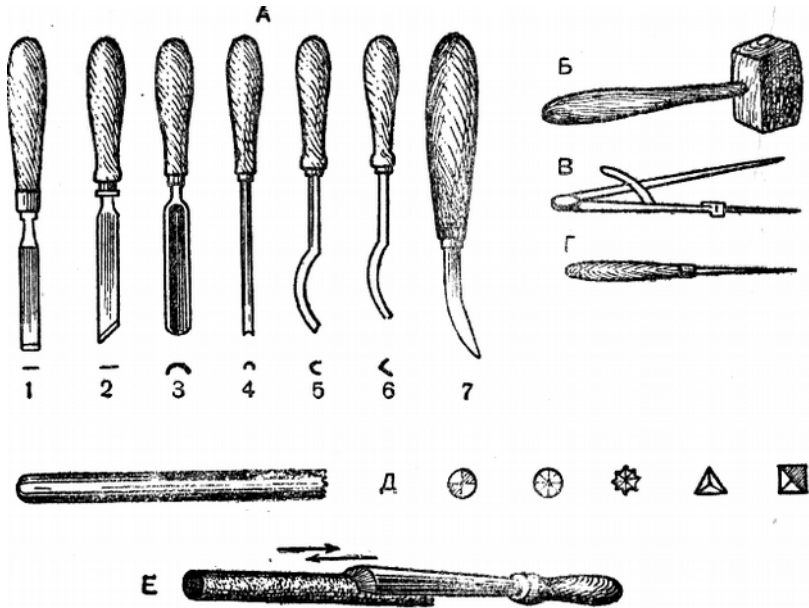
Инструменты и приспособления для резьбы по дереву:
